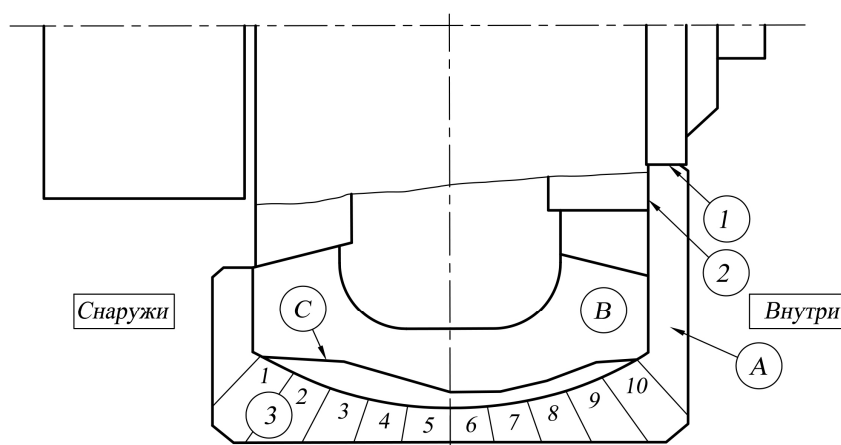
Схема измерения износа рабочей поверхности бандажа валка мельницы: А — шаблон для бандажа; В — бандаж мелющего валка; С — линия фронта износа бандажа; 1, 2 — базовые поверхности; 3 — маркировочные линии, в направлении которых измеряется величина износа; “внутри” — сторона бандажа валка относительно вертикальной оси мельницы
